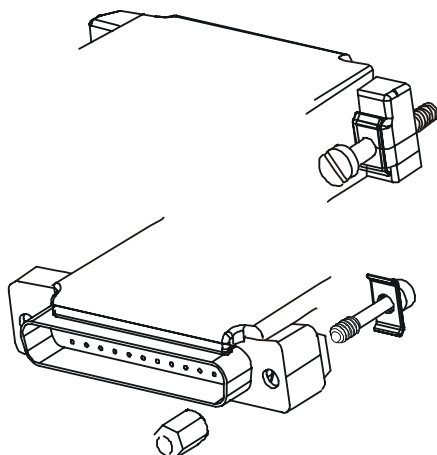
Disposición de tornillería para equipos con puerto D-SUB25 hembra.
